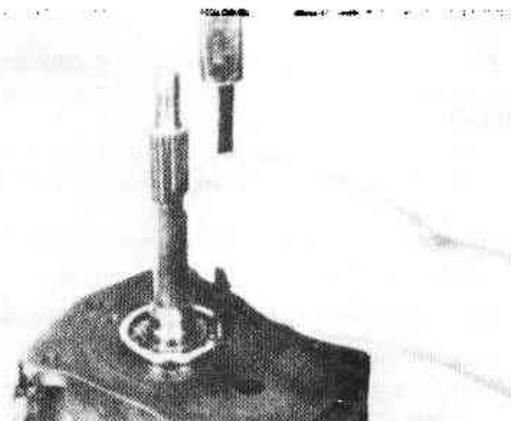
Снятие ведущего вала — коробка передач типа С (Разд.3)
